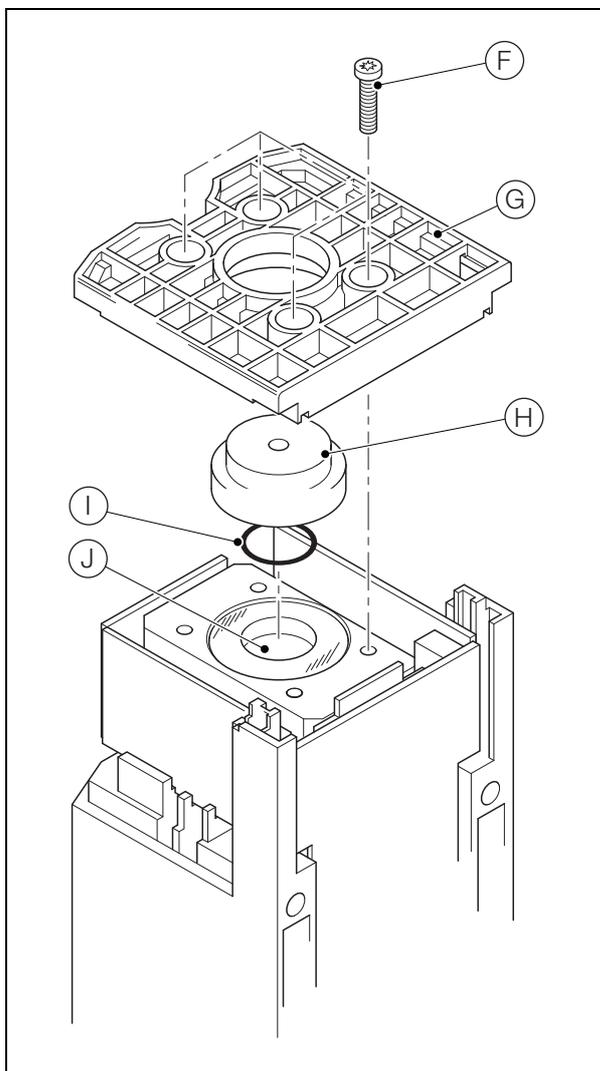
Ausbauen der Messzellen-Grundplatte
